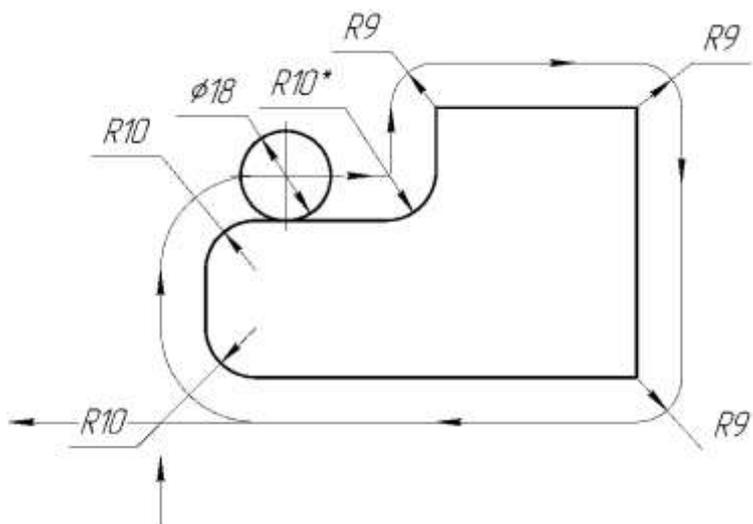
Схема выбора диаметра фрезы для чистового контурного фрезерования
